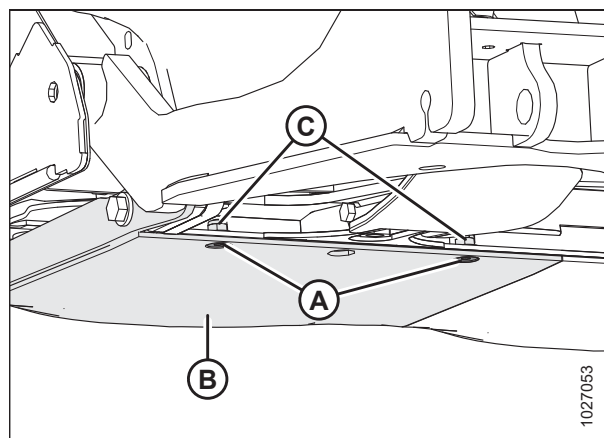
Левый наружный защитный палец – Вид сзади
